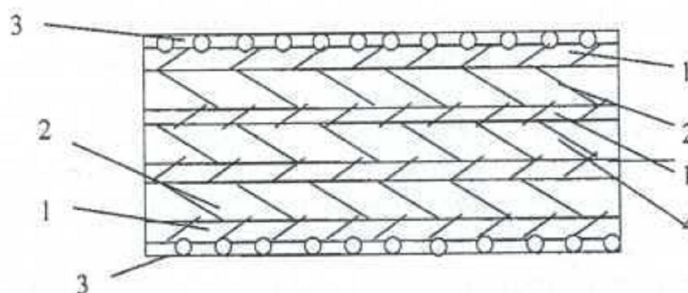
Схема сборки пакета шпона с огнезащитным покрытием:
